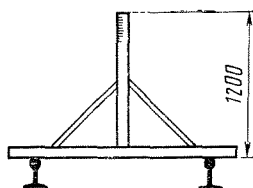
Рейка для определения высоты автосцепки над головками рельсов
